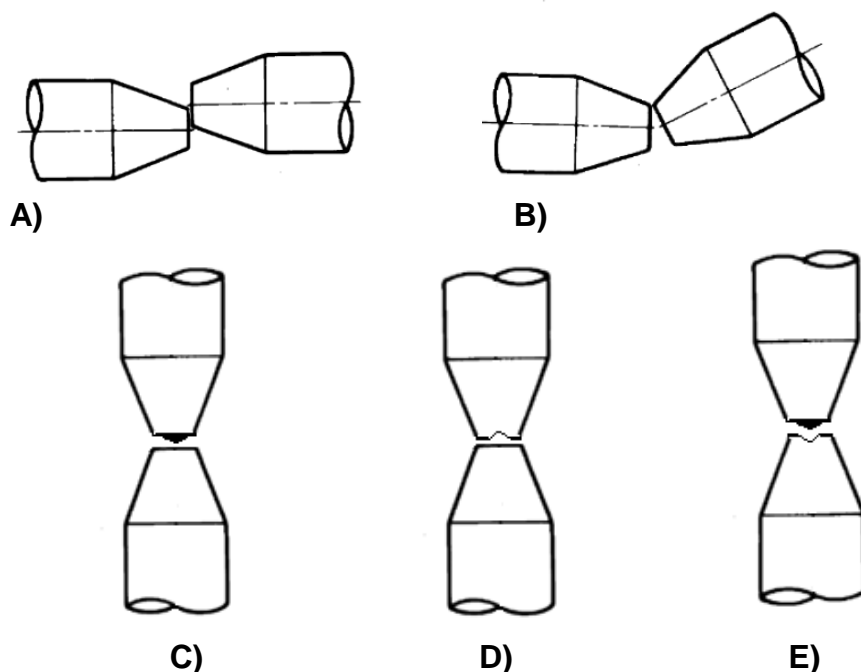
Condiciones de soldadura deficiente.
